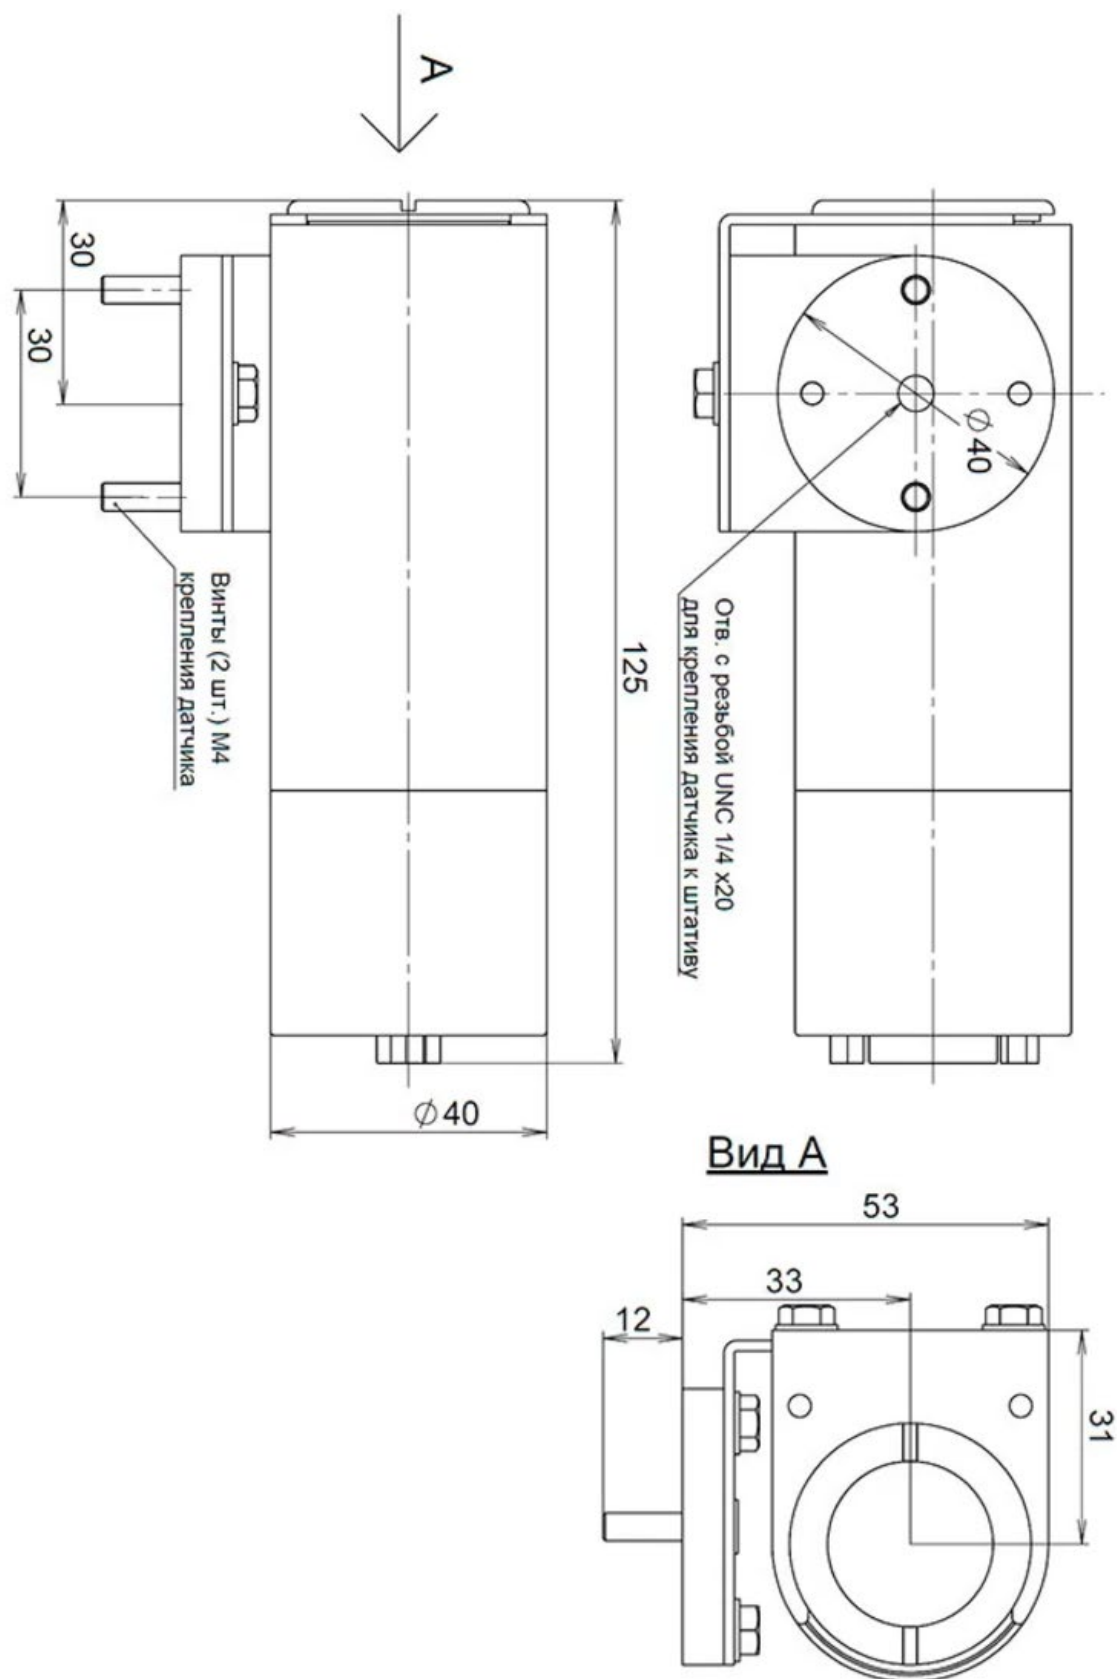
Габаритный чертеж датчика и кронштейна
